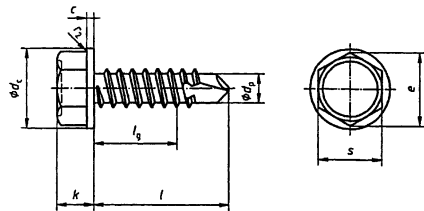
Bohrerschraube nach DIN EN ISO 15480
